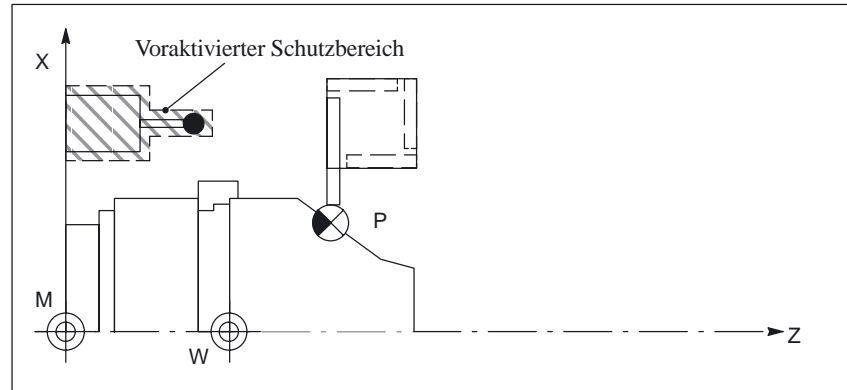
Beispiel für Drehmaschine: Voraktivierter Schutzbereich für Werkzeugmeßtaster
